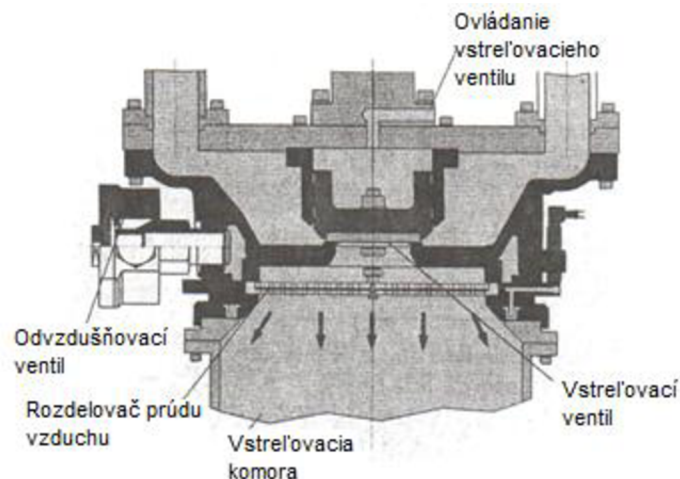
Zhutňovanie CB jadier pod tlakom. [1]
